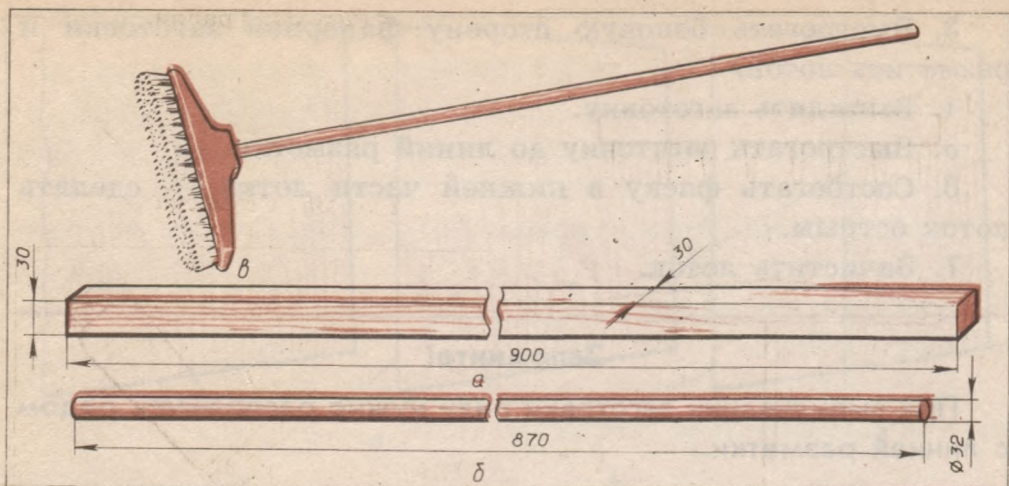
Круглая ручка для щетки: а — заготовка; б — круглая палка; в — применение ручки.
